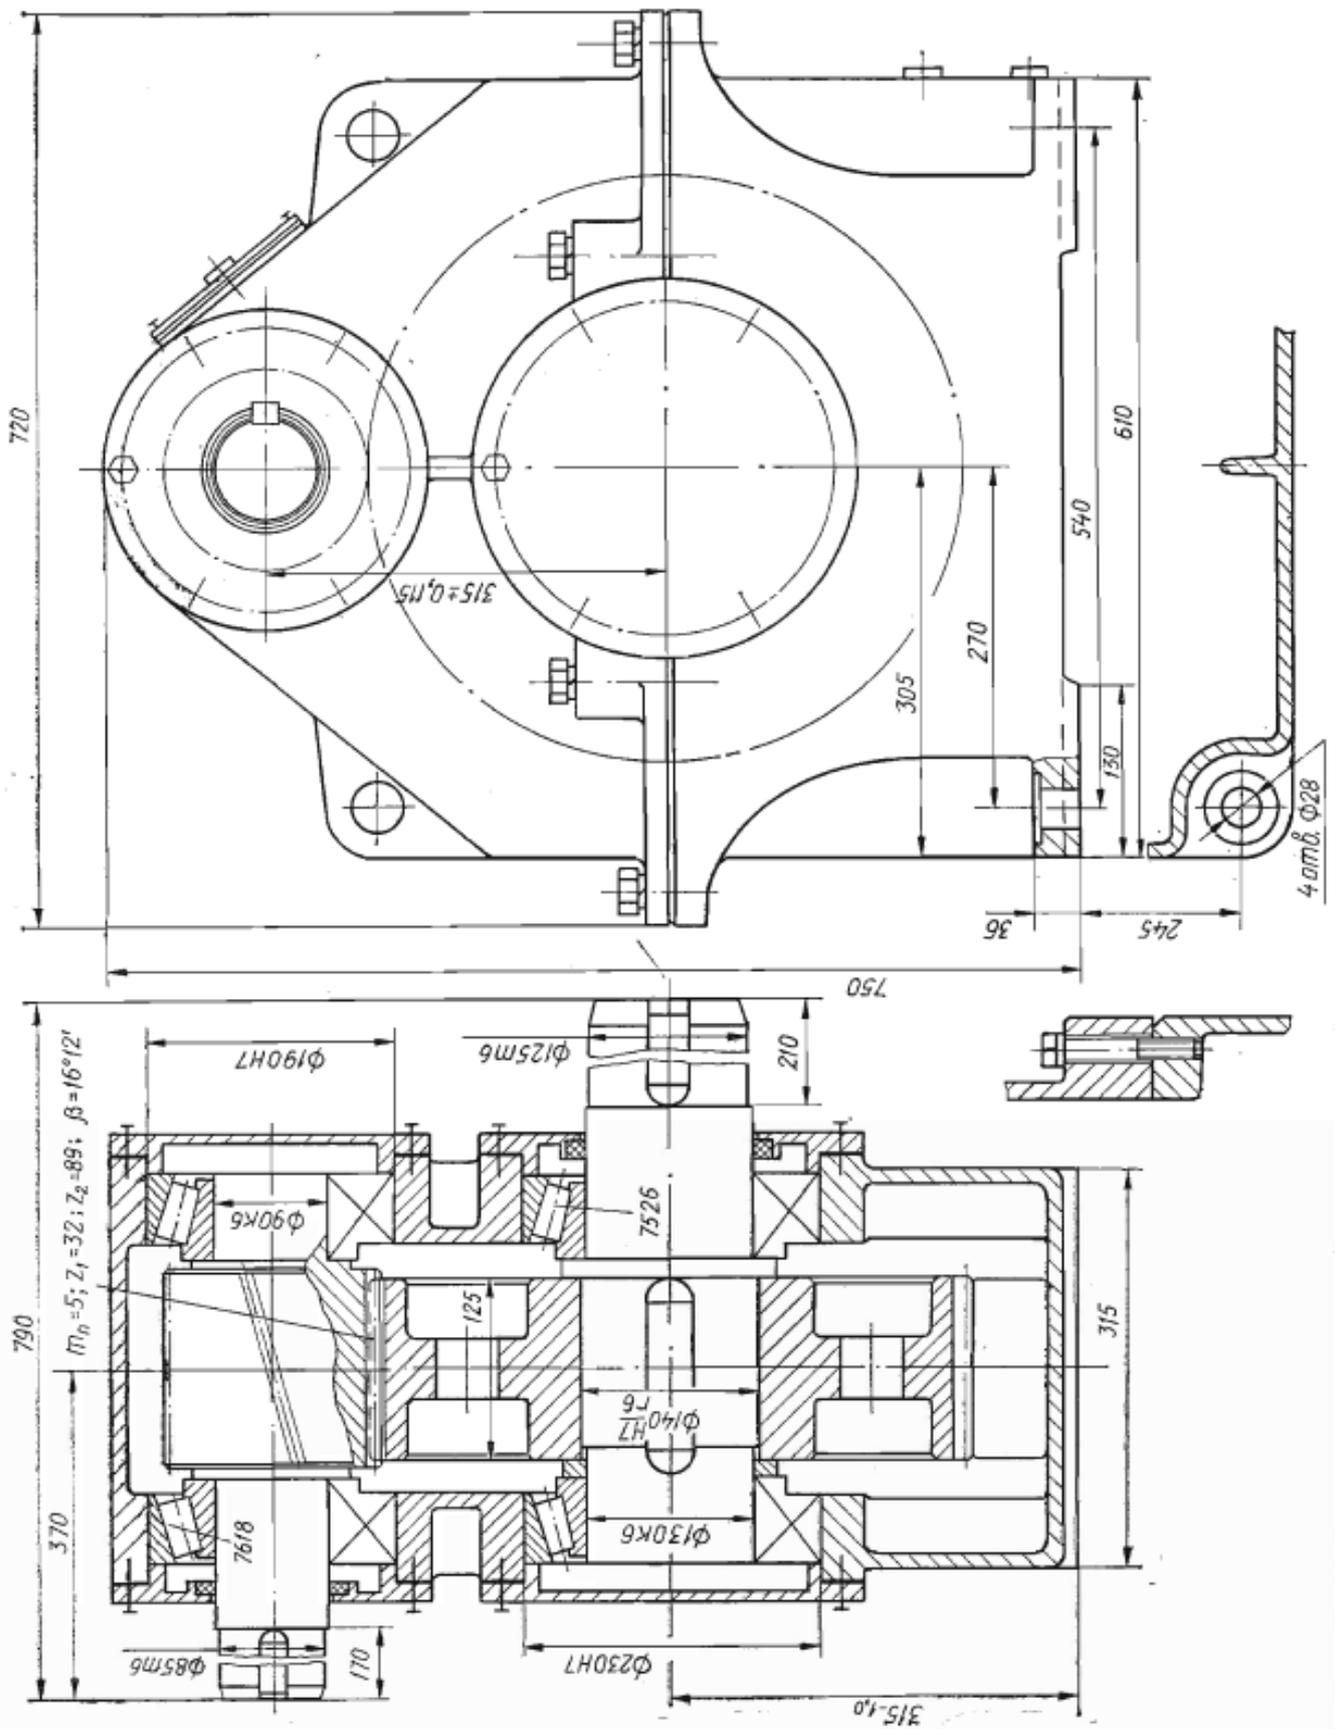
Редуктор с верхним расположением шестерни
